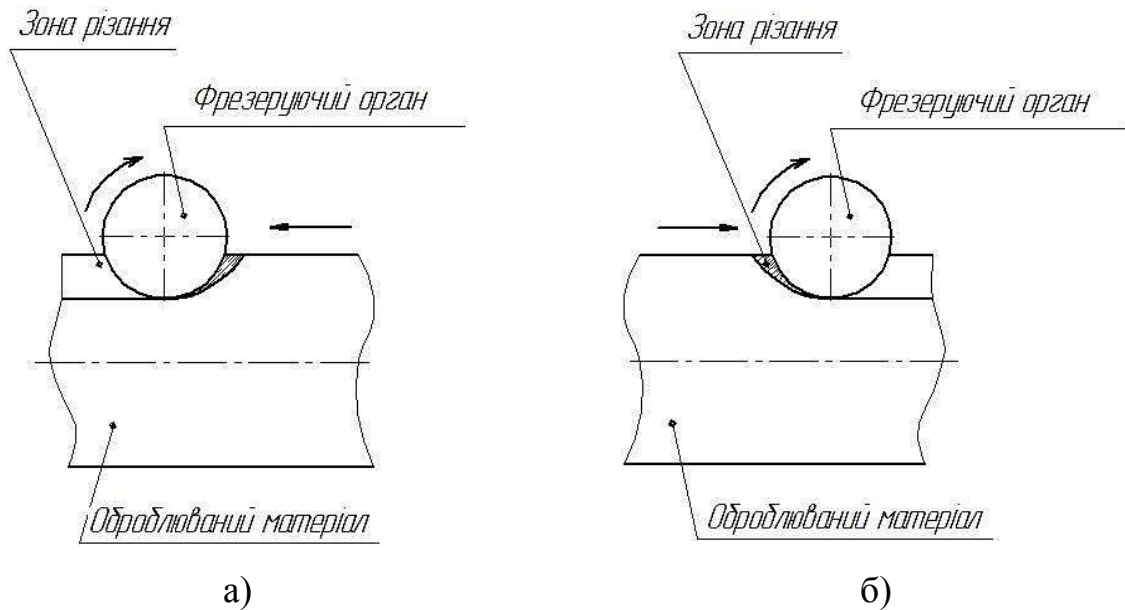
Існуючі типи фрезерування: а) попутне фрезерування; б) зустрічне фрезерування.
